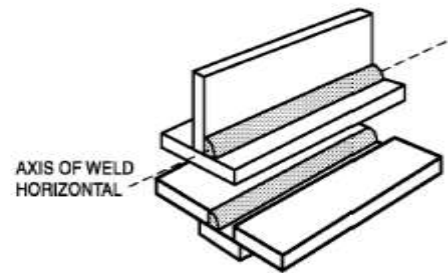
Posición de las pruebas en planchas de Soldadura por Ranura (9).
